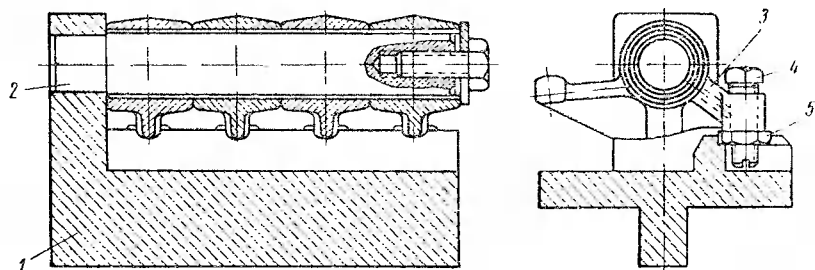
Приспособление для подборки коромысел с регулировочными винтами:
